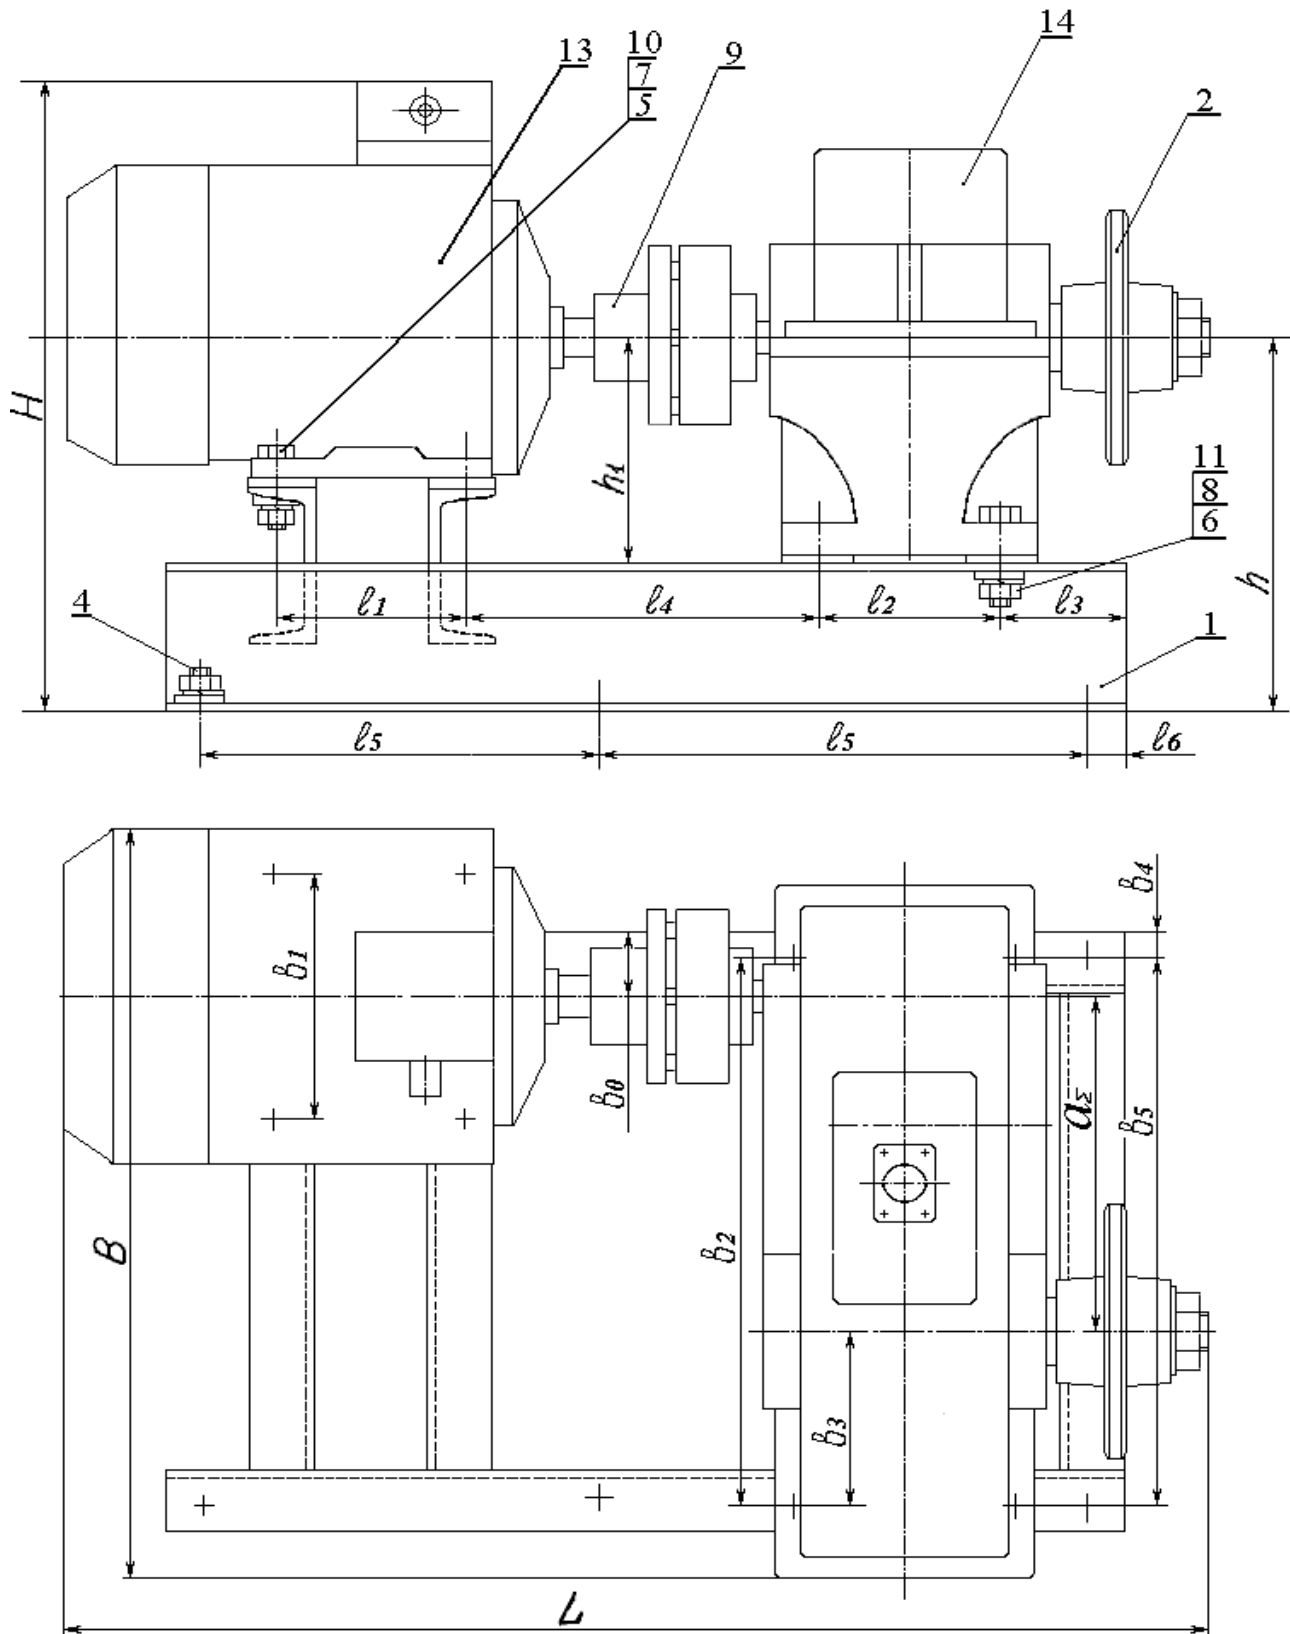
Пример оформления чертежа привода с редуктором 1Ц2У и цепной передачей
